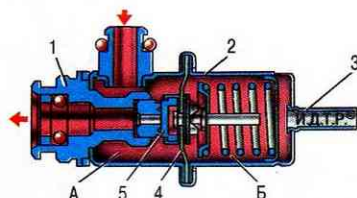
Регулятор давления топлива: 1 — корпус; 2 — крышка; 3 — патрубок для вакуумного шланга; 4 — диафрагма; 5 — клапан; А — топливная полость; Б — вакуумная полость
